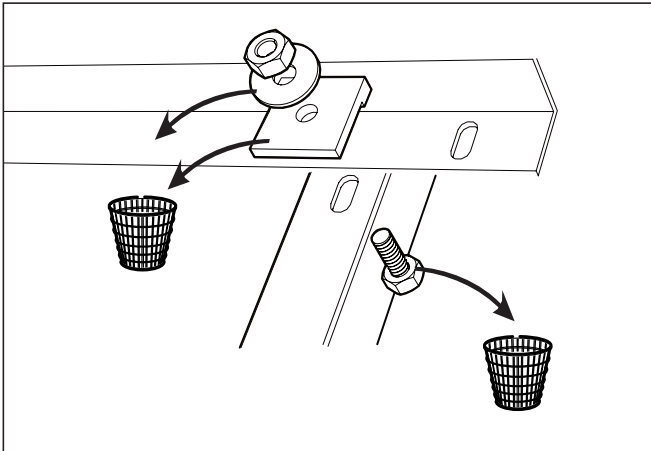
Schrauben und Befestigungsklemmen entfernen
